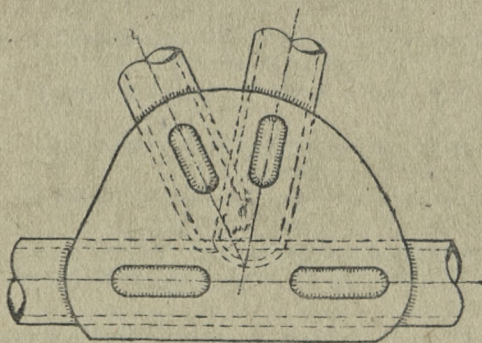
Увеличение длины сварного шва при помощи прорезей
